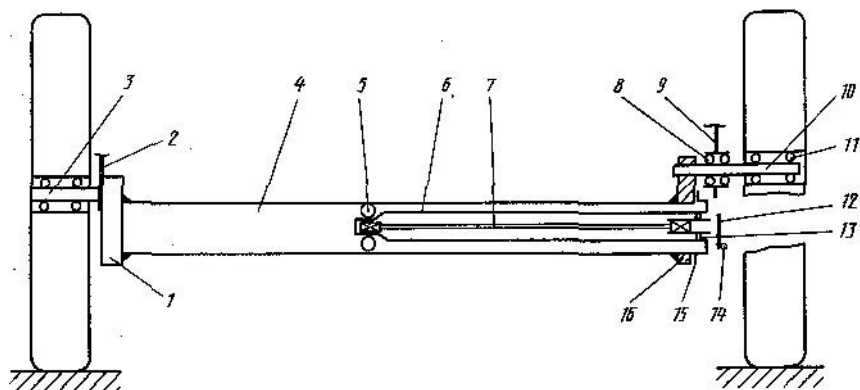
На автомобиле «Хонда-цивик» труба 4 соединяет опоры 1 и 16 подшипника колеса. Левый продольный рычаг 2 подвижно привернут к детали 1. При крене кузова правый рычаг 9 поворачивается на цапфе 10
